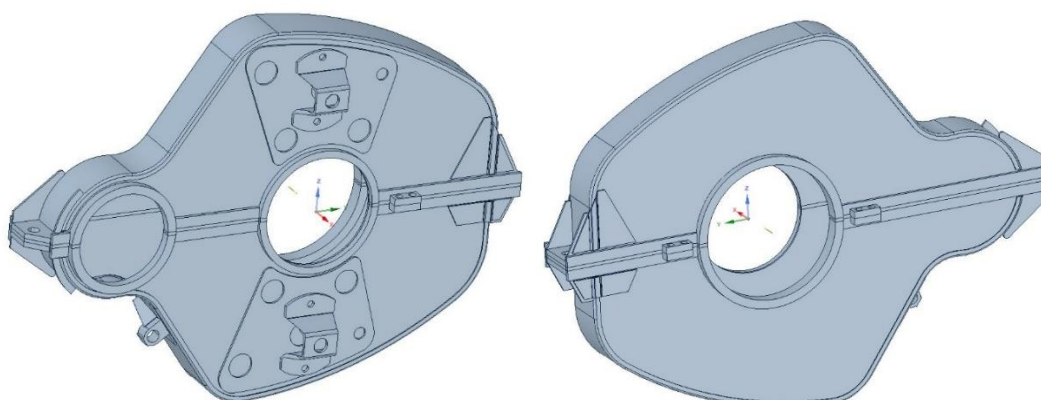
Серийно выпускающийся кожух 5ТС.300.214, изготовленный из гнутых стальных листов методом сварки
